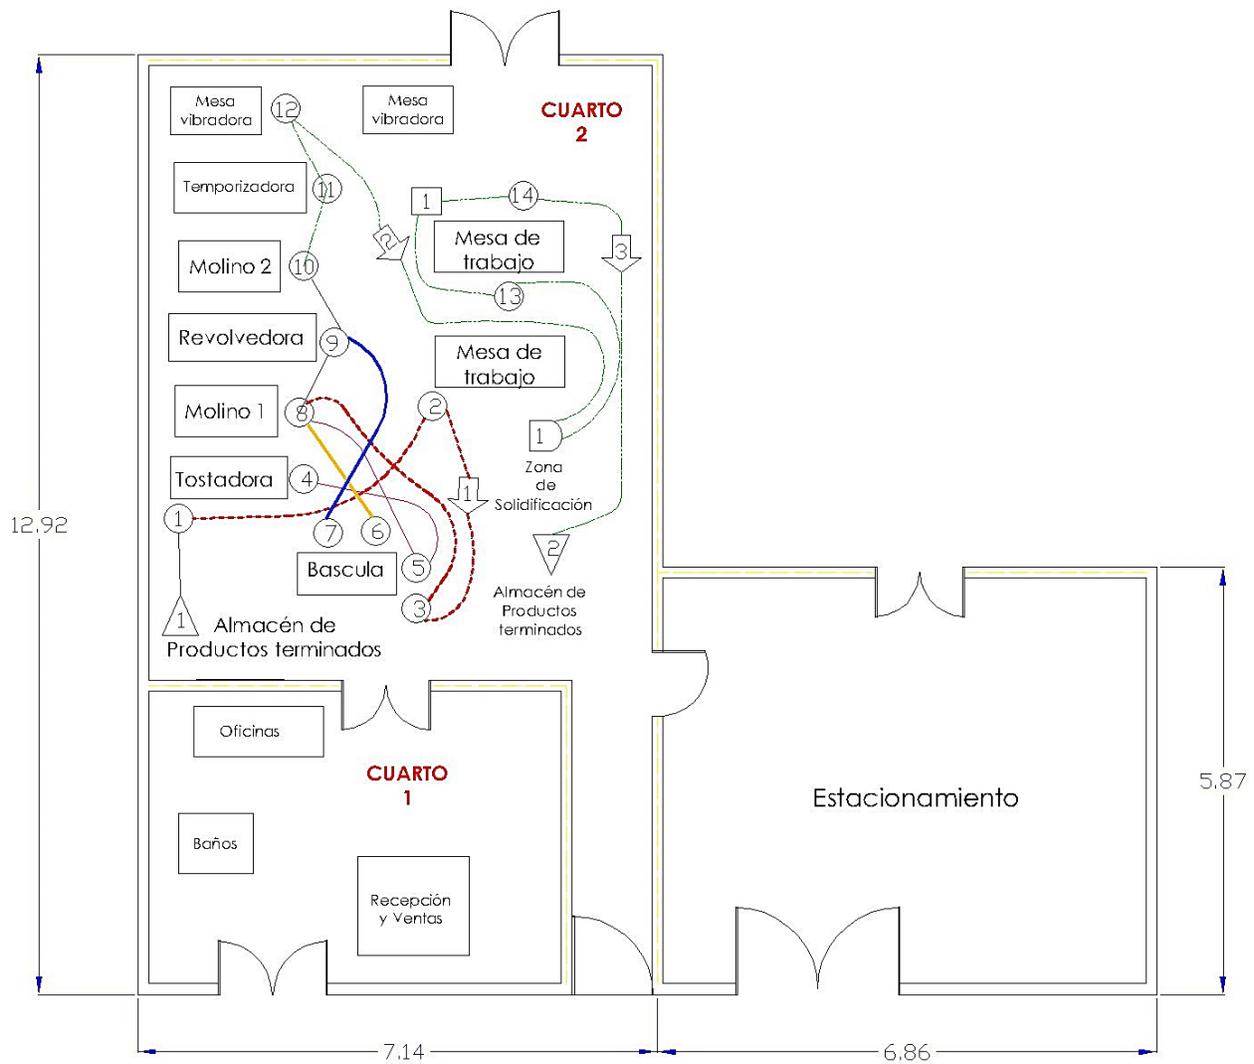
Propuesta de distribución de planta (Fuente: Tesista).
